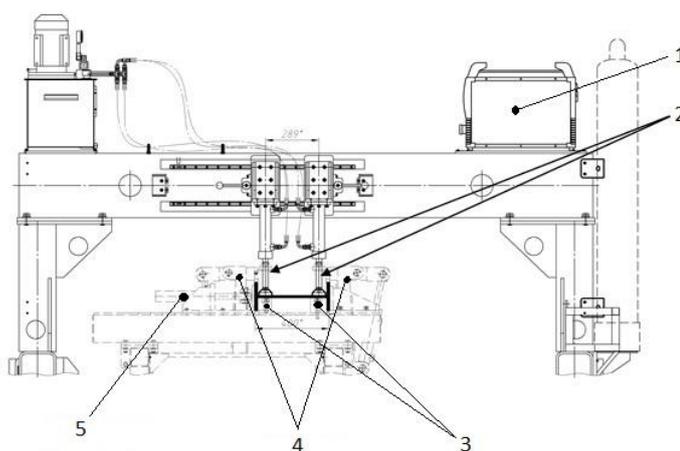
Схема сборки лонжерона рамы с расположением узлов АКСЛ-3, где 1 – сварочный аппарат, 2 – гидроцилиндры, 3 – регулируемые опоры, 4 – прижимы вертикальные, 5 – гидроцилиндр.
